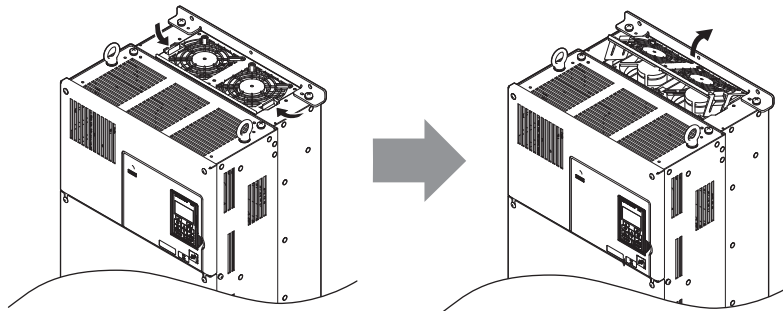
Extracción de la cubierta del ventilador de refrigeración: 4A0094, 4A0114
